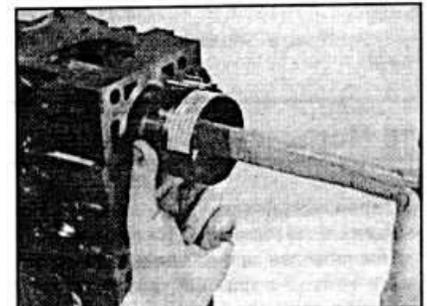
D.79. Установка поршня в цилиндр с использованием деревянной ручки молотка.
